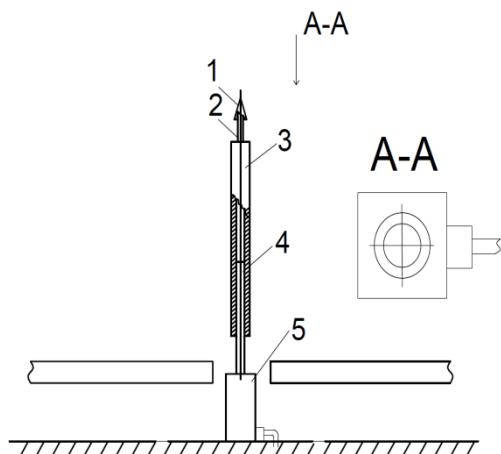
Кокс на резьбовом валу с сервоприводом:
